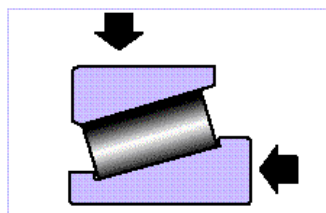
Combinación de carga radial y axial en un rodamiento cónico.
